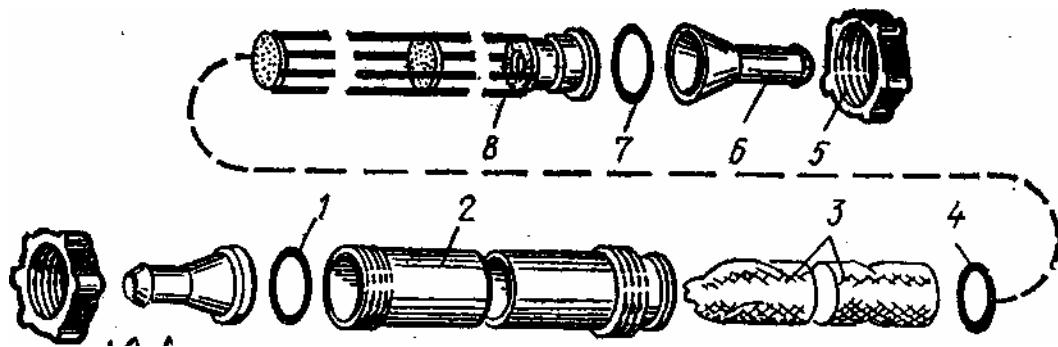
Деталі циліндричного фільтра: 1, 7 – ущільнювальні прокладки; 2 – корпус; 3 – фільтруючий елемент; 4 – кільце; 5 – гайка; 6 – перехідник; 8 – каркас
